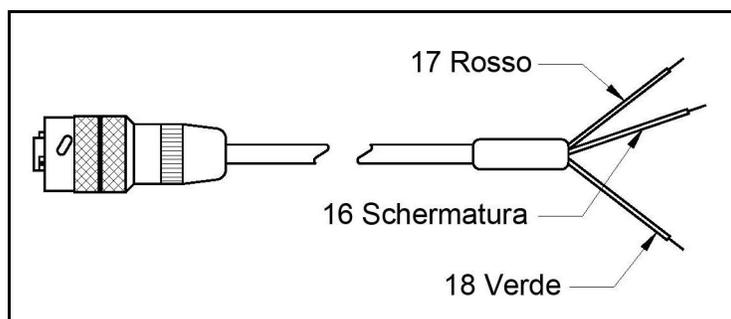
Collegamento dei cavi della sonda igrometrica all'ossido di alluminio
